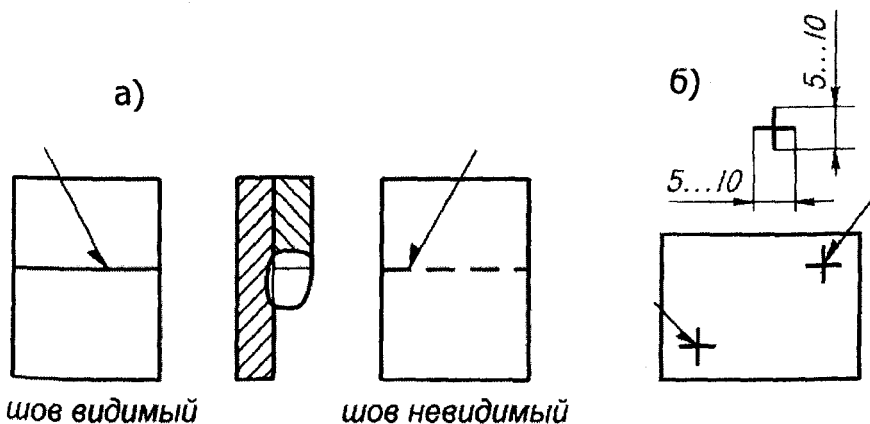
Условные изображения шва сварного соединения или одиночной сварной точки:
